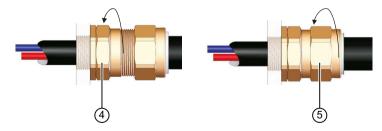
Cavi: Fasi 2 e 3 dell'installazione:
